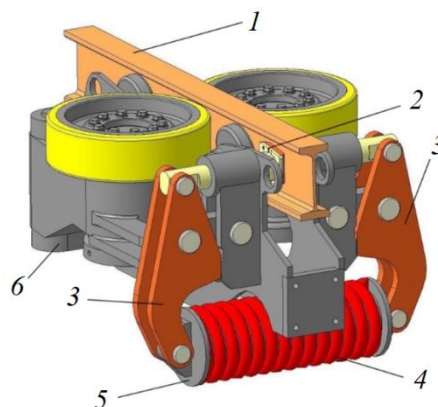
Общий вид тормозного устройства, установленного на тяговой тележке:
